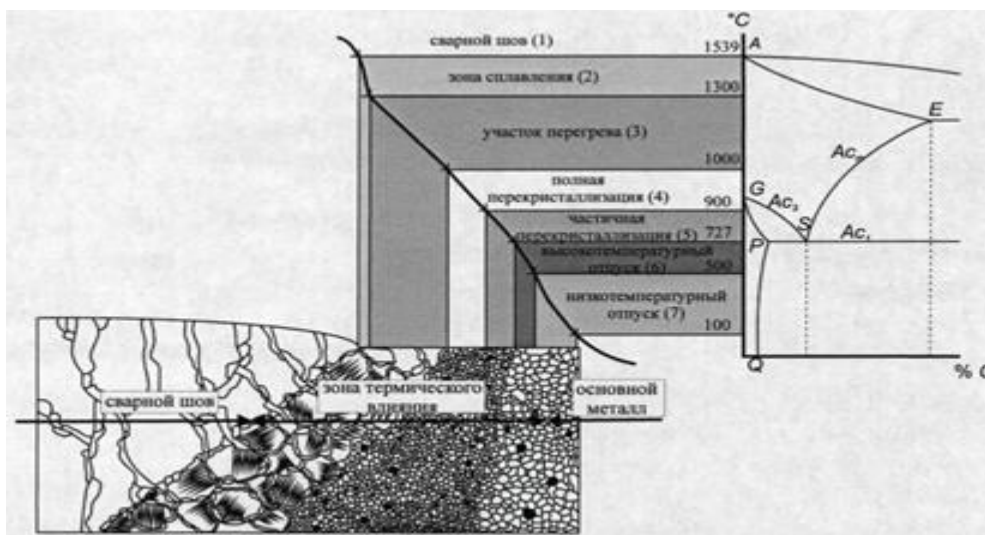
Схематическое изображение сварного соединения из низкоуглеродистой стали, полученного электродуговой сваркой
